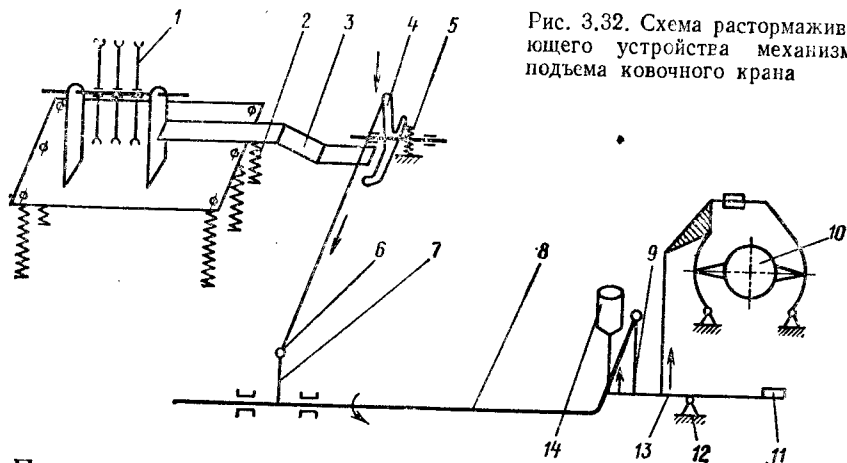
Схема растормаживающего устройства механизма подъема ковочного крана
